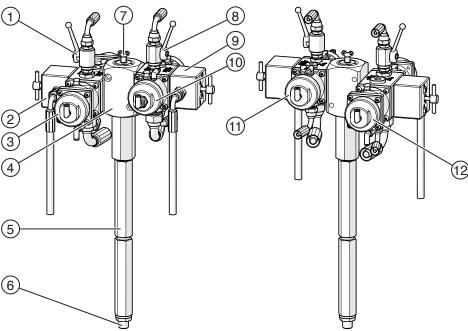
Vues avant et arrière de l'unité de mélange standard (exemple)
